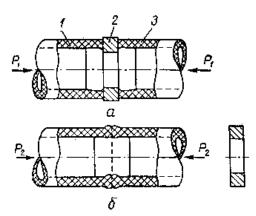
Схема сварки труб встык при нагреве соединяемых поверхностей нагретым инструментом:
